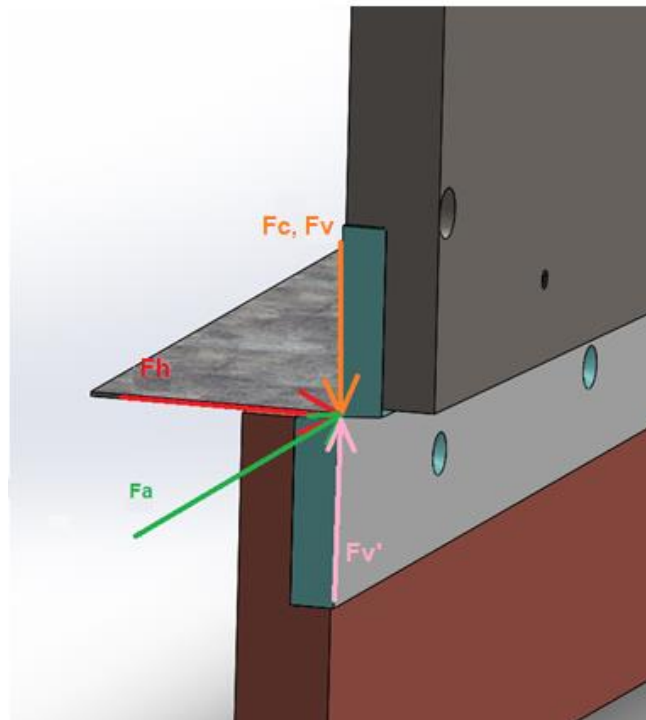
Corte por cuchilla inclinada zona de corte – fuerzas
